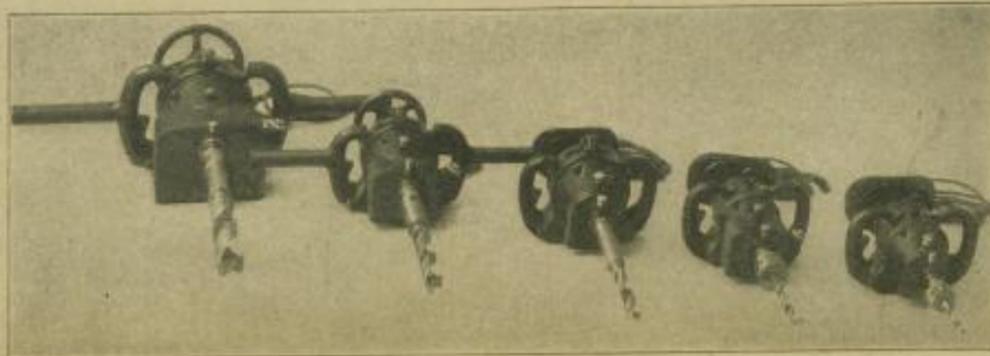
Hand-Bohrmaschinen mit Spannülse oder Brustschild, sowie bügelförmigen Handgriffen mit Ausschalter und Umschalter
